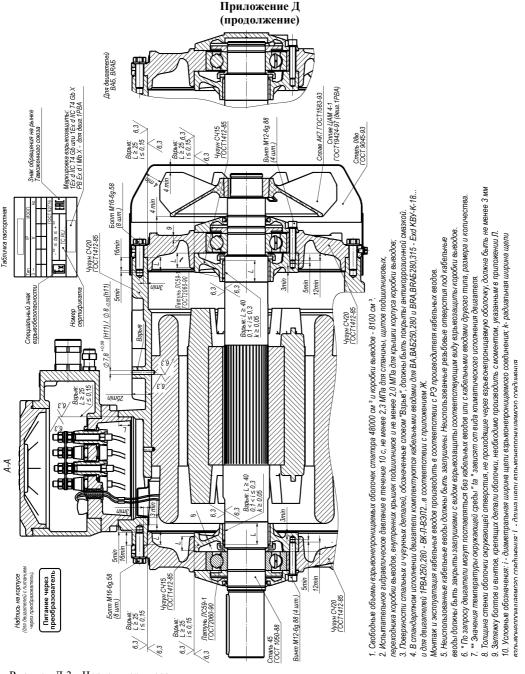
Чертеж взрывозащиты двигателей ВА(Б),1PBA250,280; BRA(Б),1PBRA280,315
